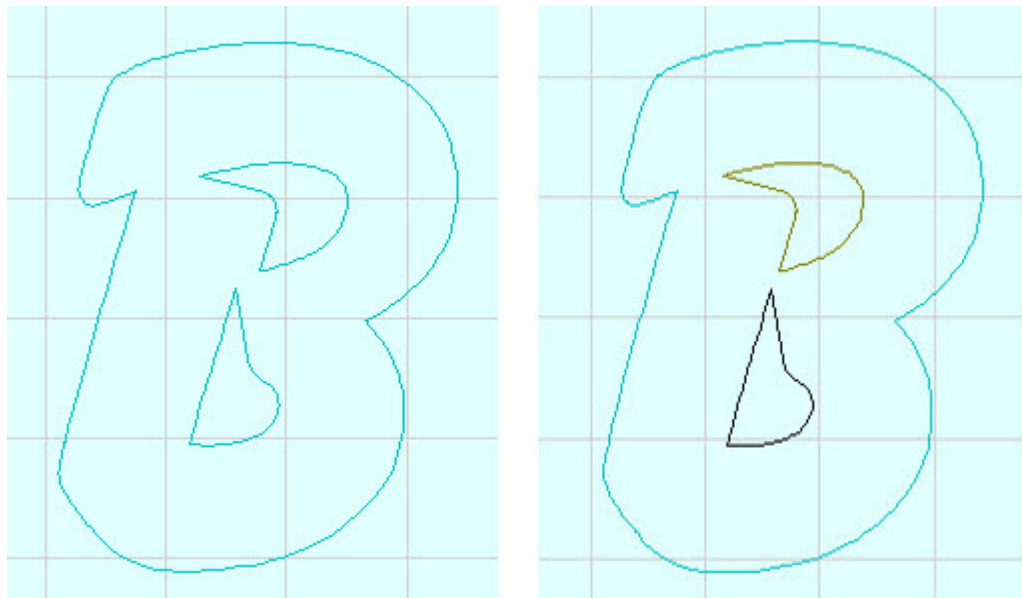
Links nur ein Werkzeug, rechts mehrere Werkzeuge
